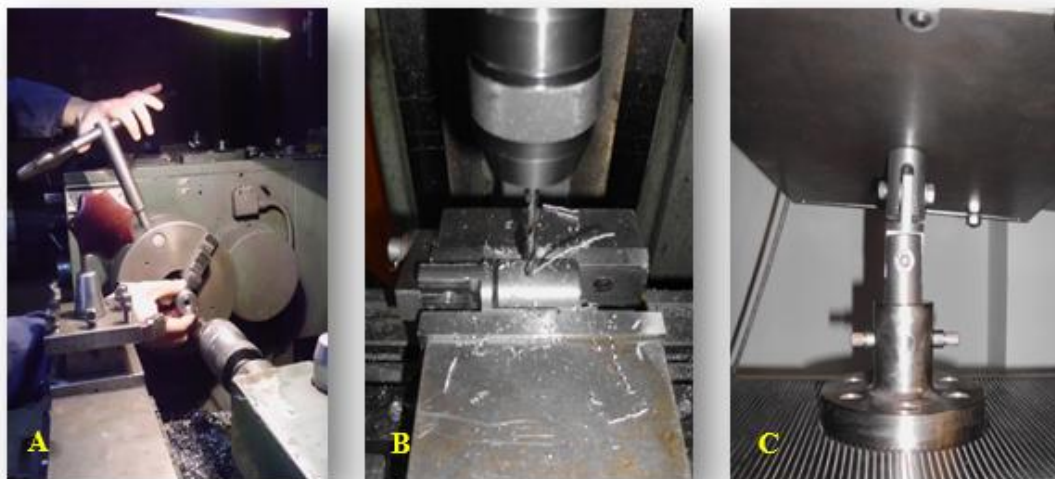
Etapas de fabrico do sistema mecânico rotacional; A) Elaboração de um cilindro com 31,5mm de diâmetro por 200 mm de comprimento, e furo para parafuso M10; B) Maquinação do componente intermédio de ligação, fresagem e furação dos três componentes para parafusos M8; C) Sistema mecânico rotacional terminado.
